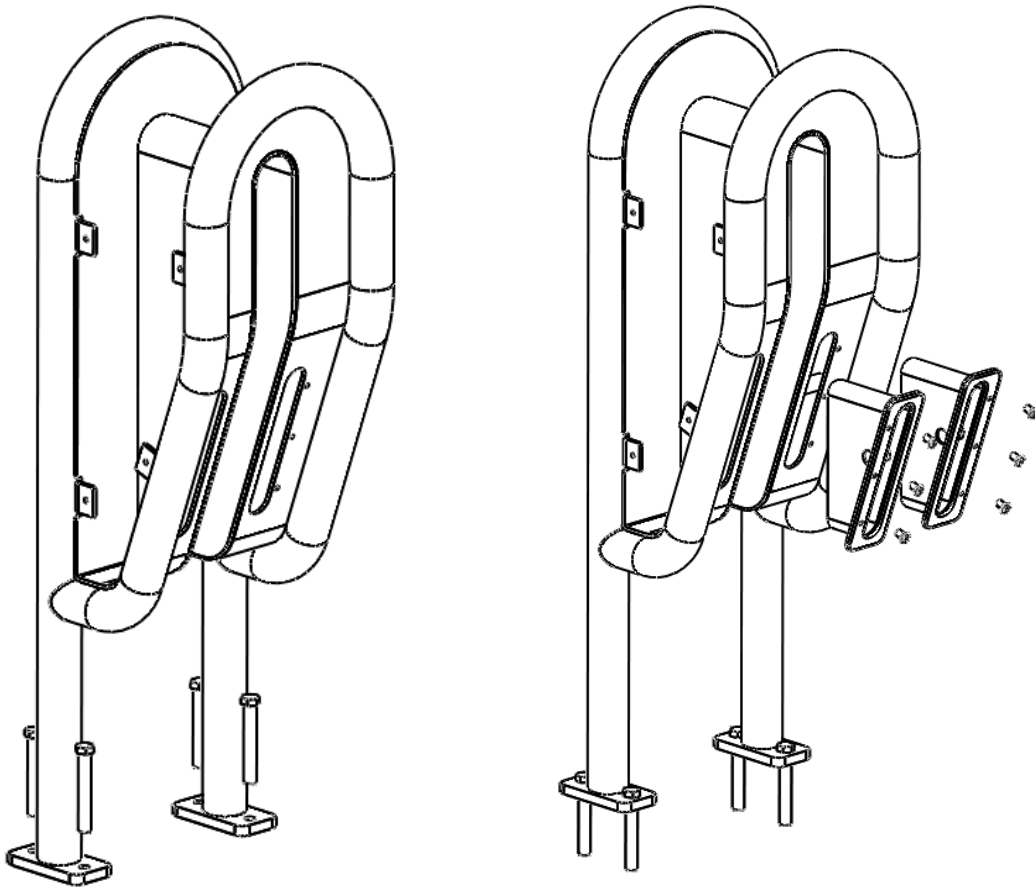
Puntos de soldadura de la carcasa frontal
